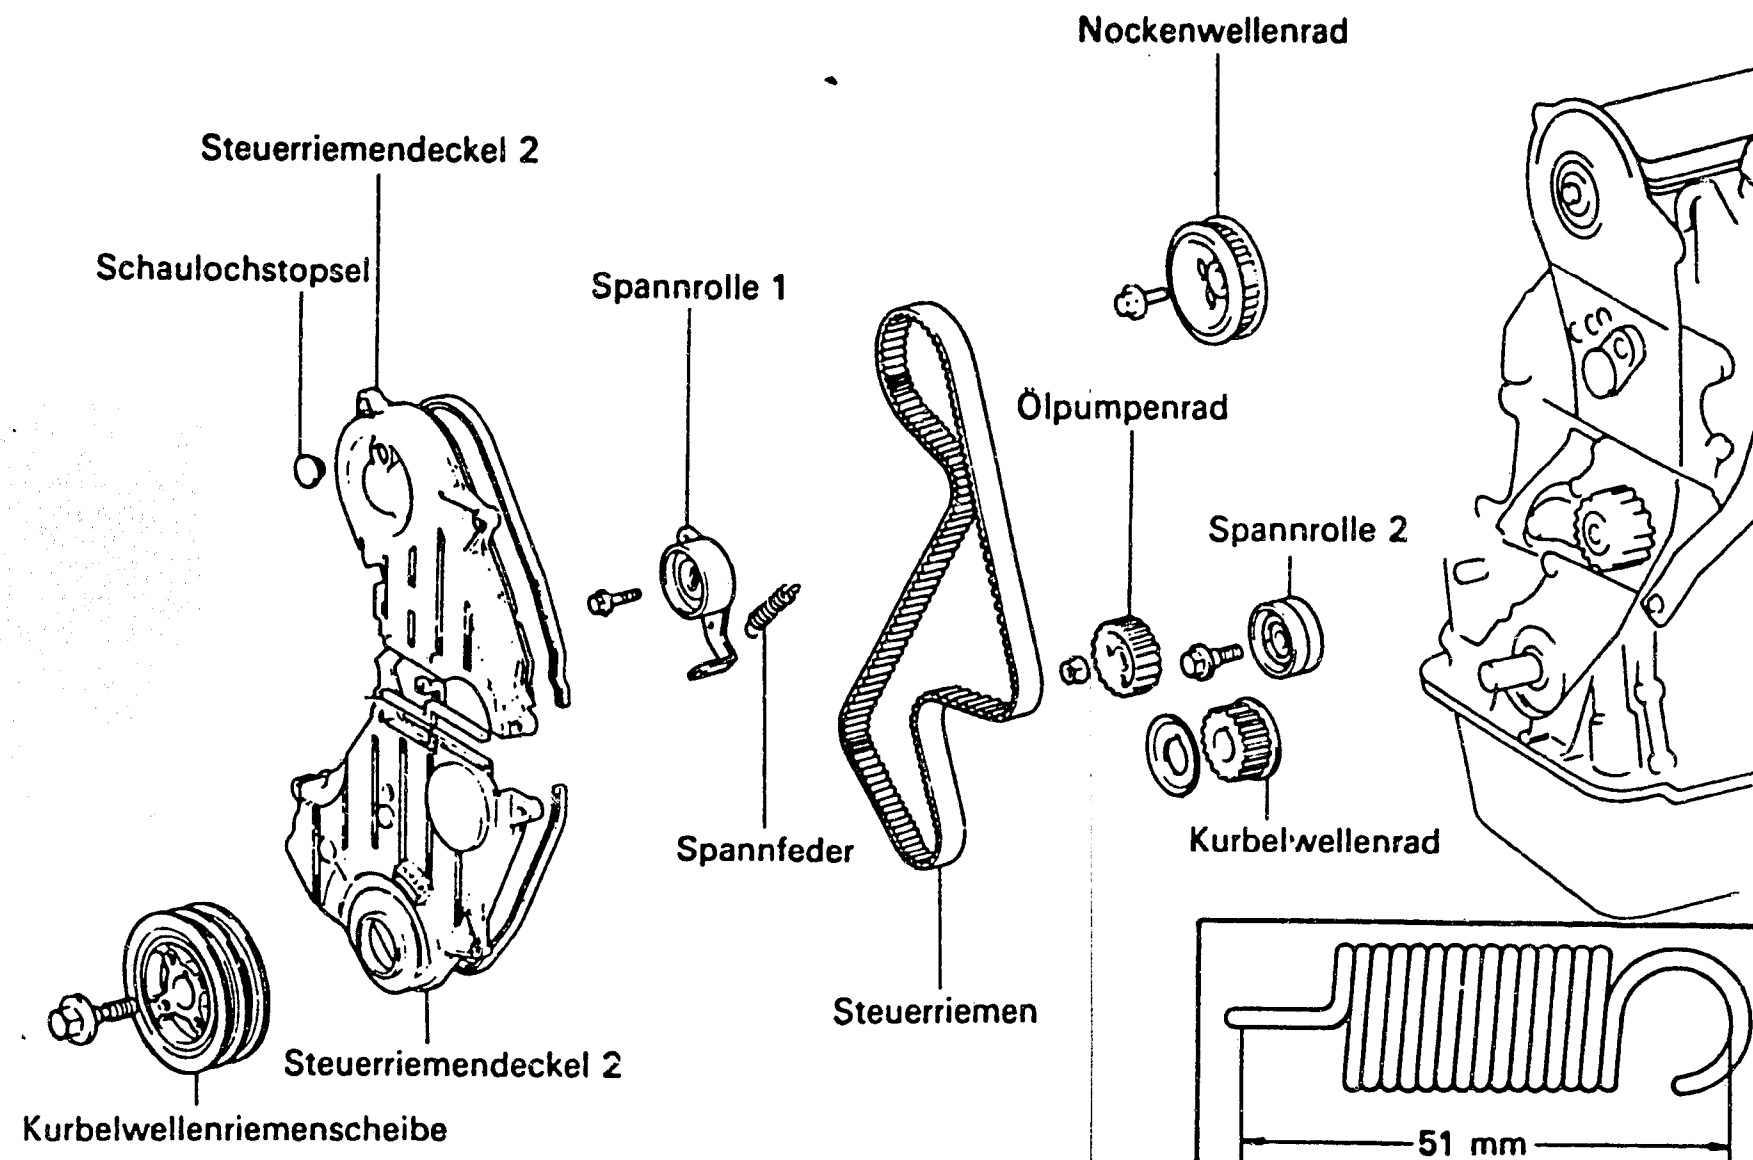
Motor 1S: Einzelteile der Motorsteuerung. Die Spannfeder des Zahnriemenspanners muss sich bei einer Zugkraft von 73...84 N auf 60 mm verlängern.
